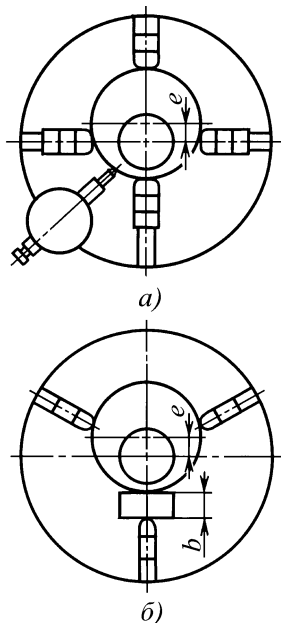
Схемы обработки эксцентрических заготовок рабочего колеса
